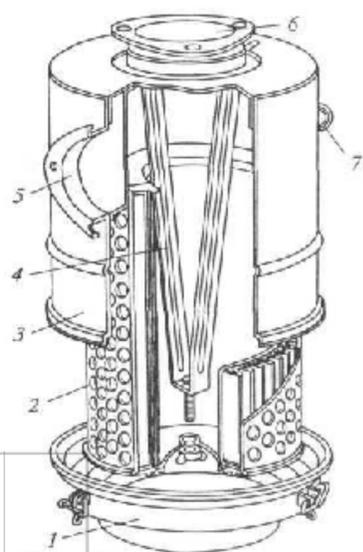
Схема системы питания дизельного двигателя воздухом: 1 - воздушный фильтр; 2 - фильтрующий элемент; 3 - решетка; 4 - труба; 5 - колпак; 6 - эжектор; 7 – цилиндр
